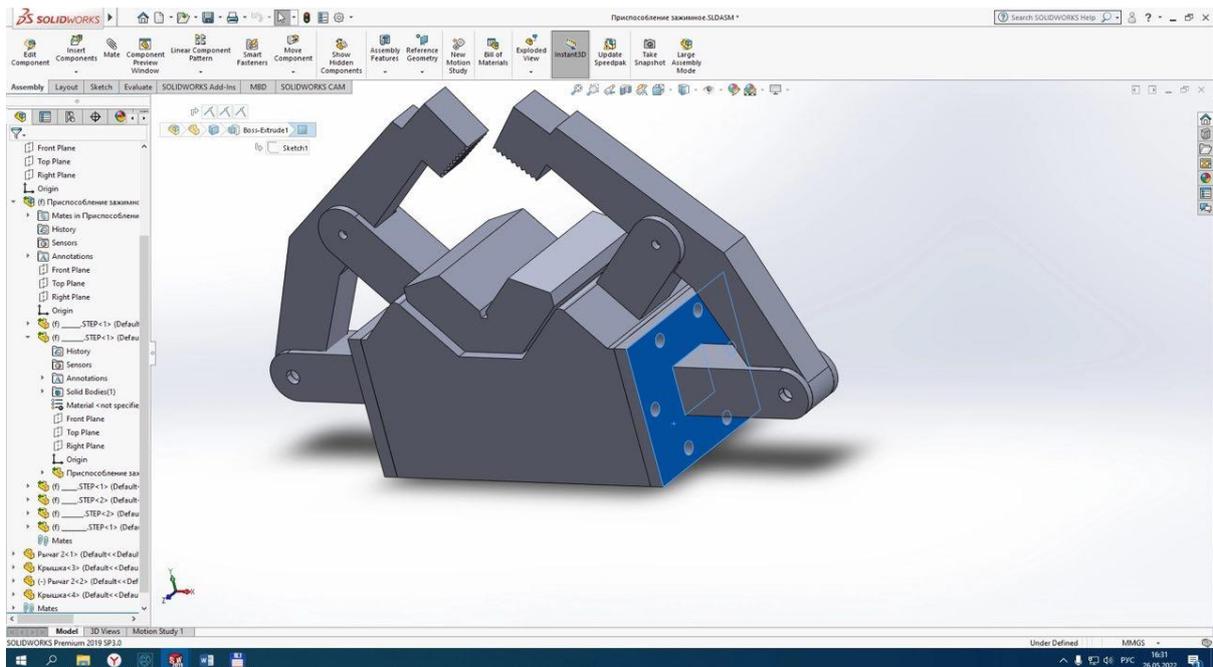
Приспособление зажимное для заготовок в 3D
